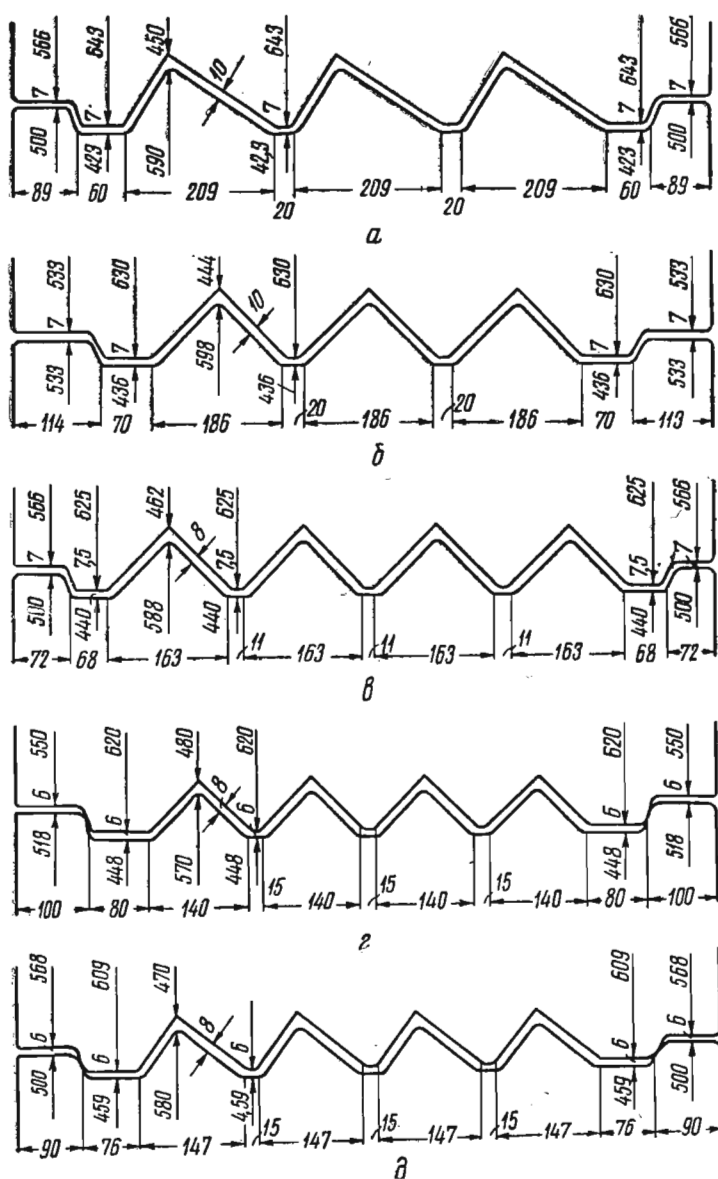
Калибровка чистовых валков для прокатки равнобокой и неравнобокой угловой стали:
